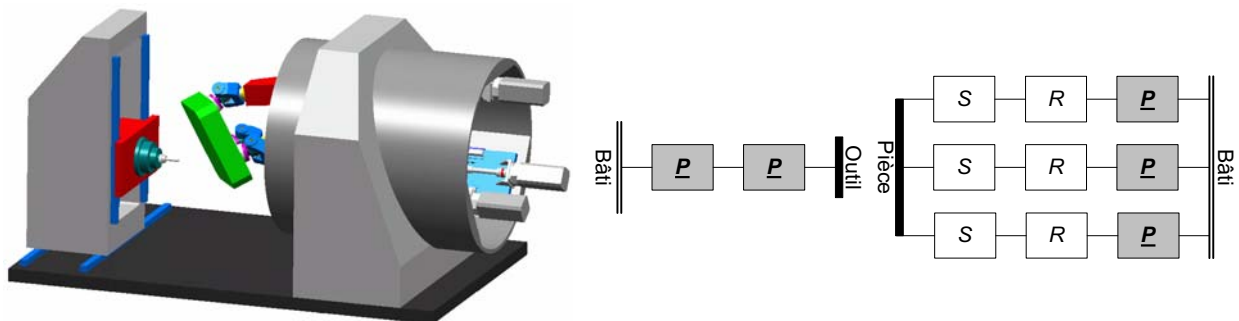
Robot 5 axes inspiré de Sprint Z3 (projet Mach21), image CAO et graphe d'agencement
